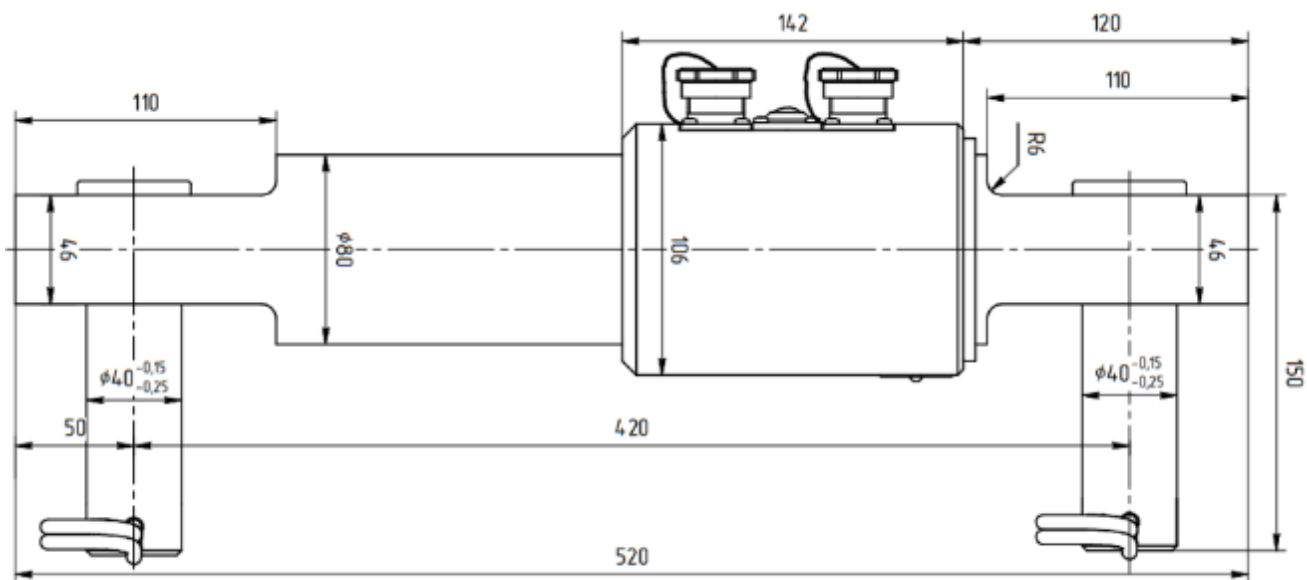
Габаритные и присоединительные размеры ДН-130В(А)
